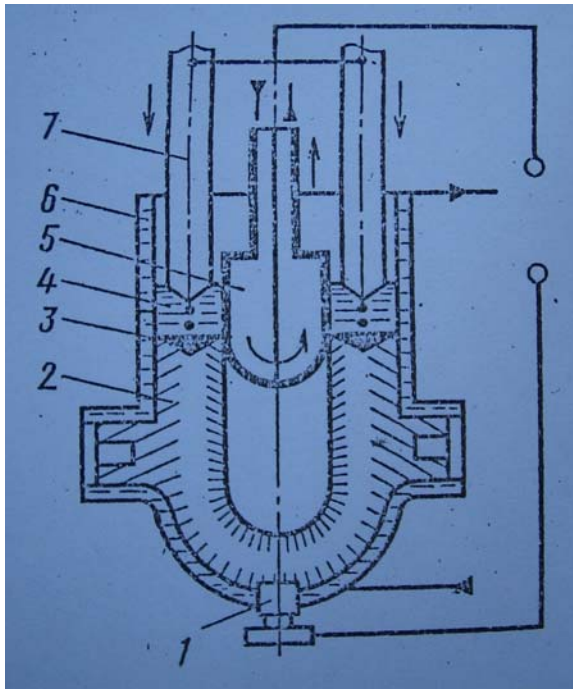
Схема получения отливки электрошлаковым литьем. 1 – затравка; 2 – отливка; 3 – расплав; 4 – шлаковая ванна; 5 – стержень; 6 – кристаллизатор; 7 – электроды.
